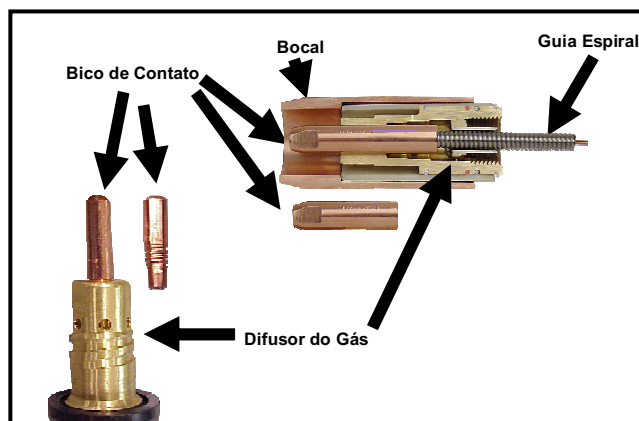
Principais componentes de uma tocha de soldagem.
